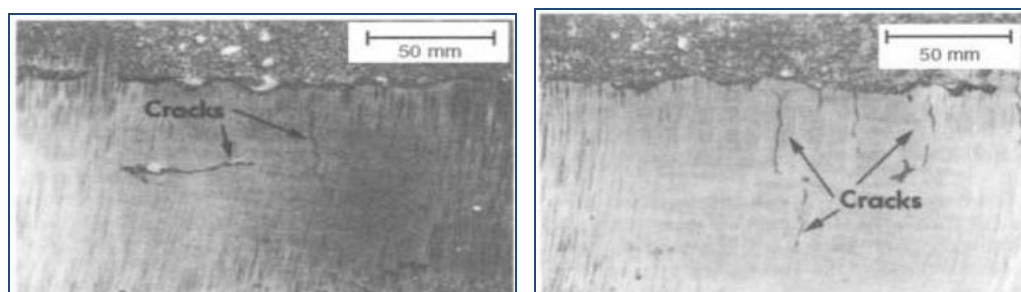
Grietas transversales que se originaron en el cordón de soldadura. [16]
